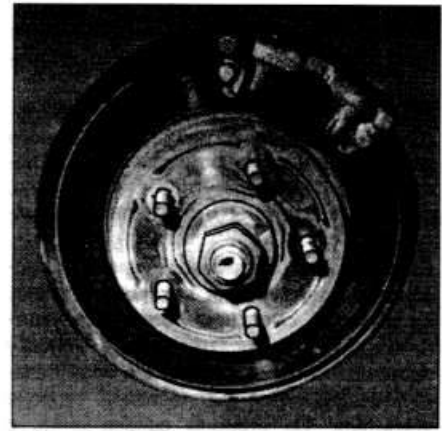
Стопорное кольцо тормозного диска заднего колеса
